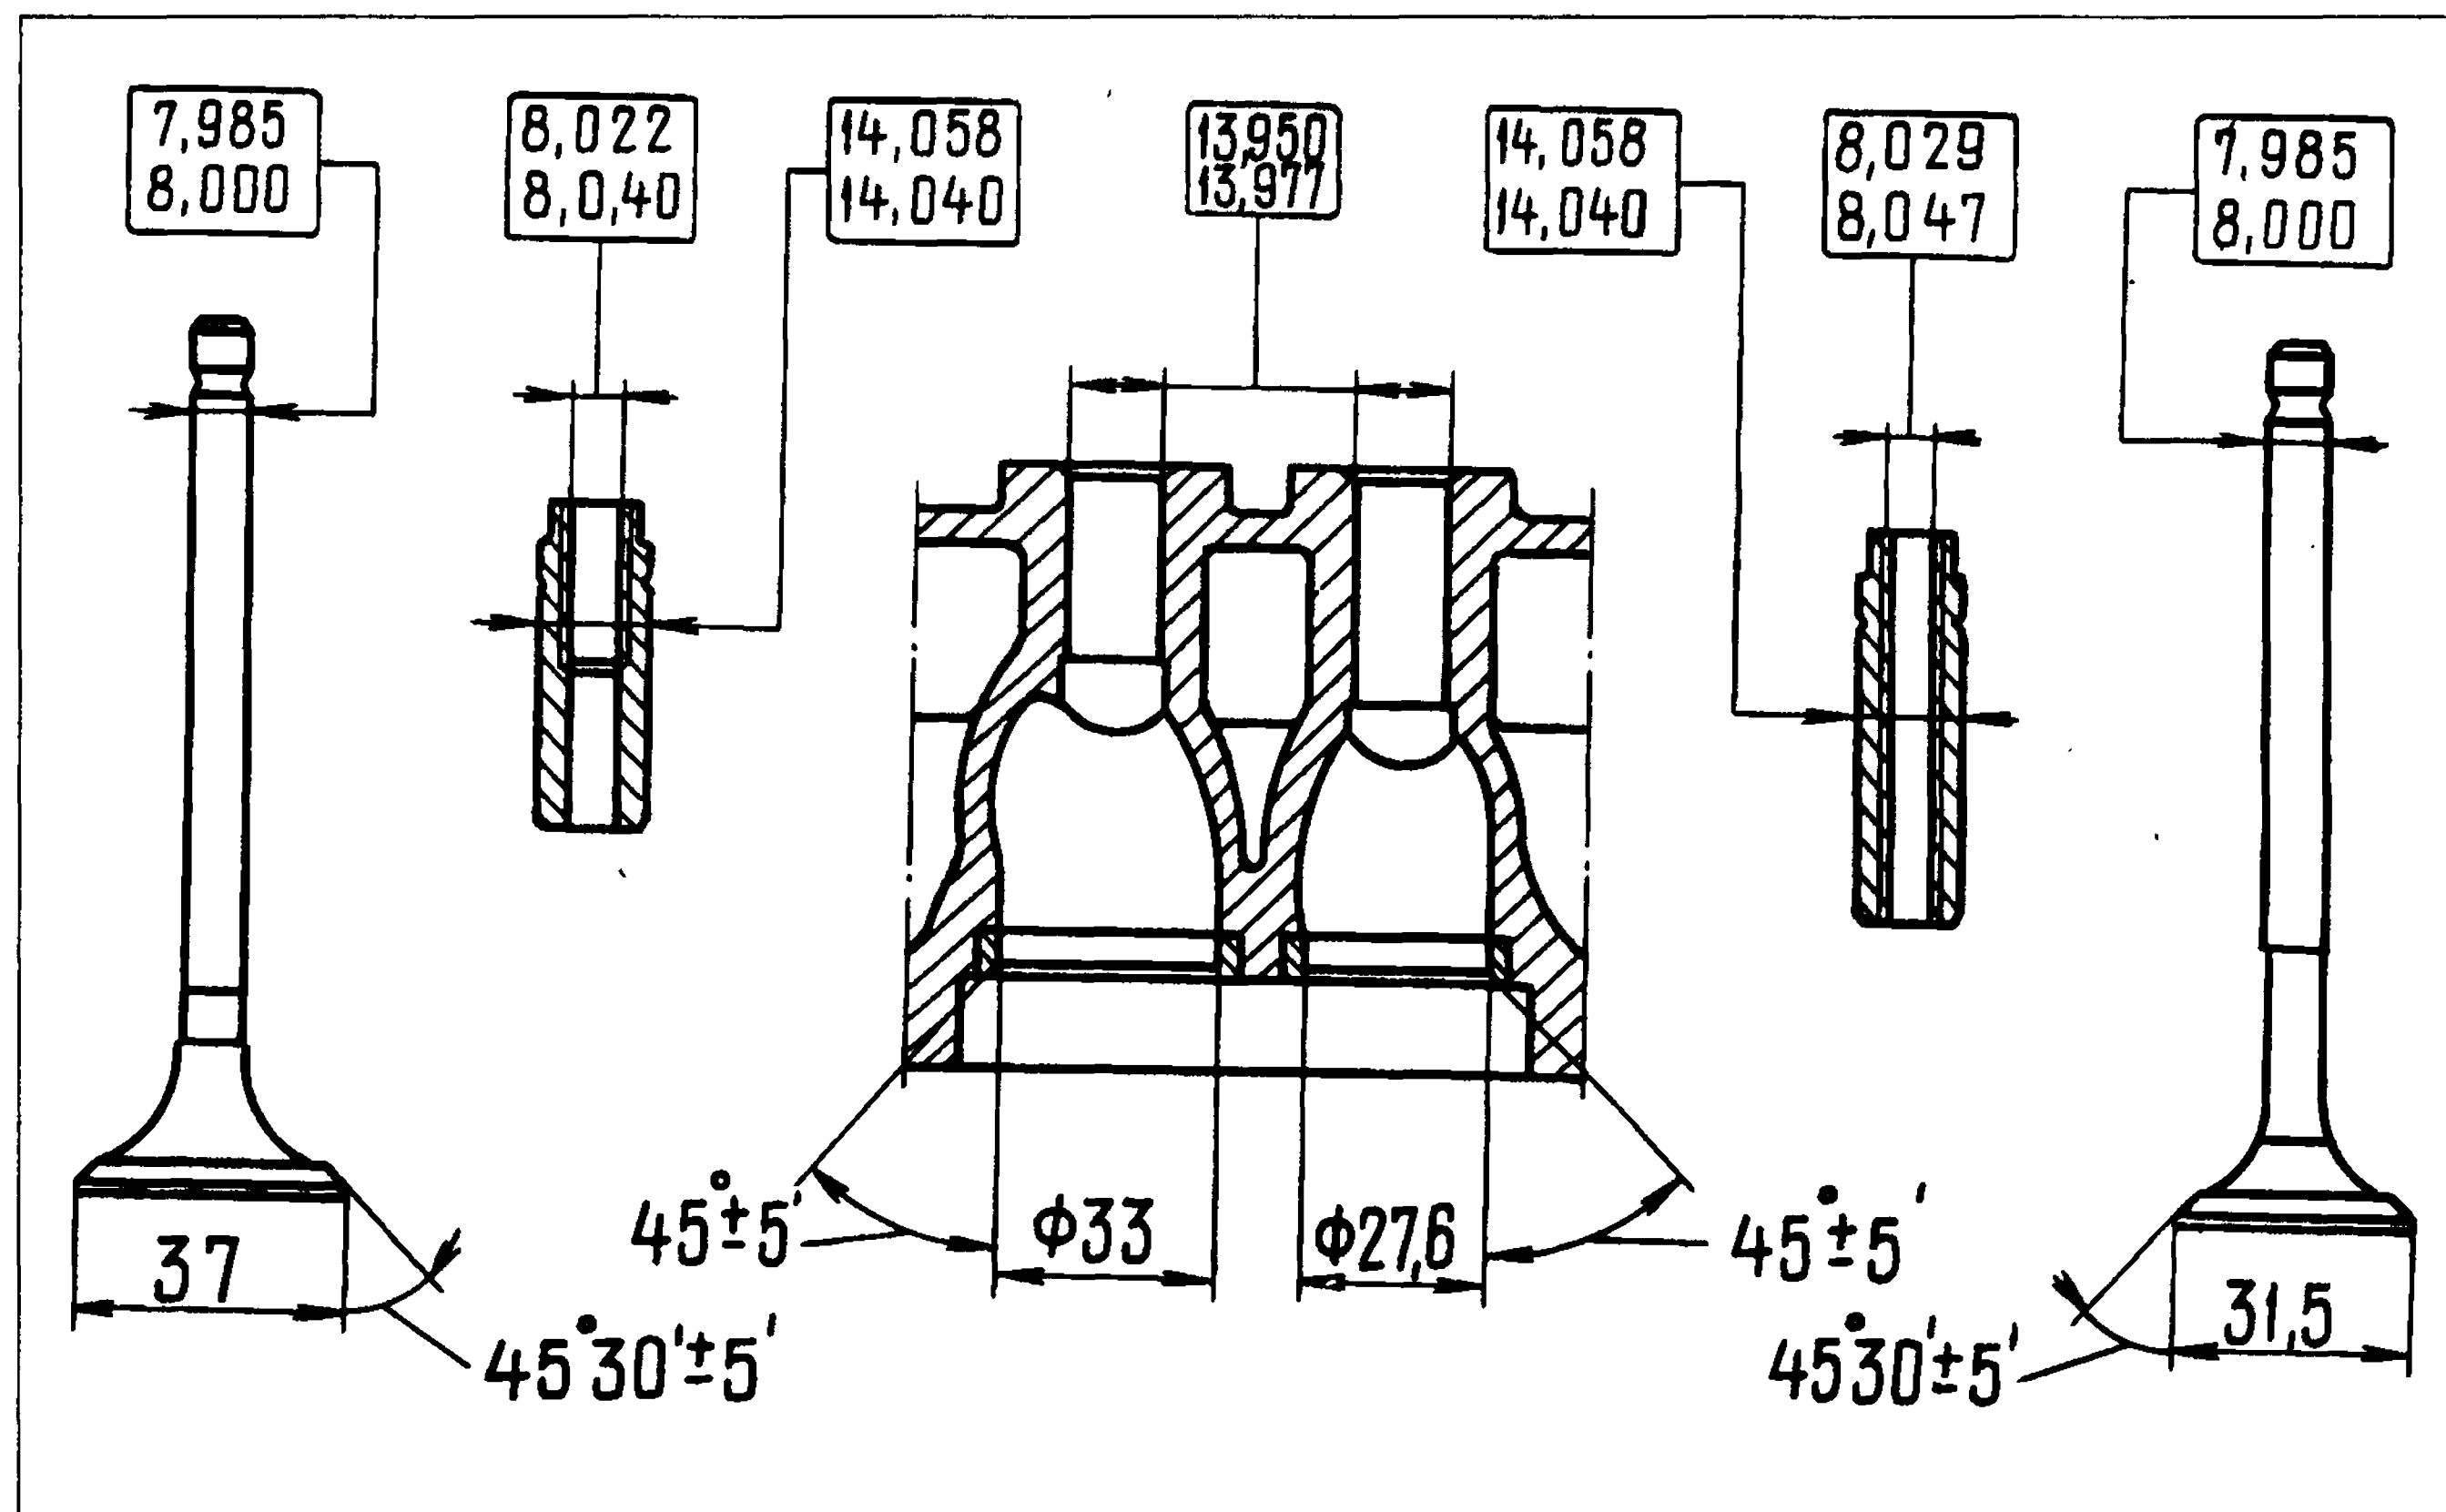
Основные размеры головки блока цилиндров, клапанов и направляющих втулок
